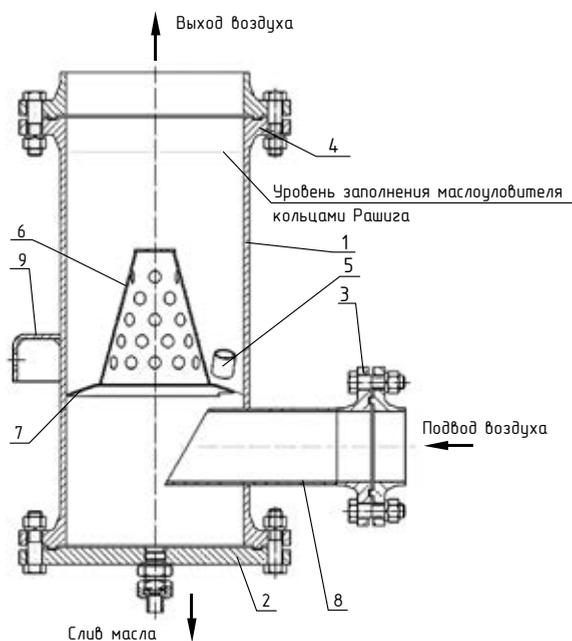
Устройство и основные габаритные размеры маслоуловителя: 1 – корпус; 2 – заглушка; 3 – фланец DN80; 4 – фланец DN200; 5 – кольца Рашига; 6 – обечайка; 7 – тарелка; 8 – патрубок; 9 – кронштейн
